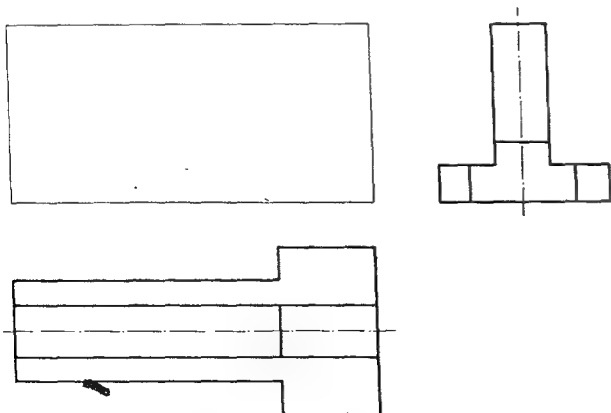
Dibujar el alzado del objeto del que se dan planta y perfil.
